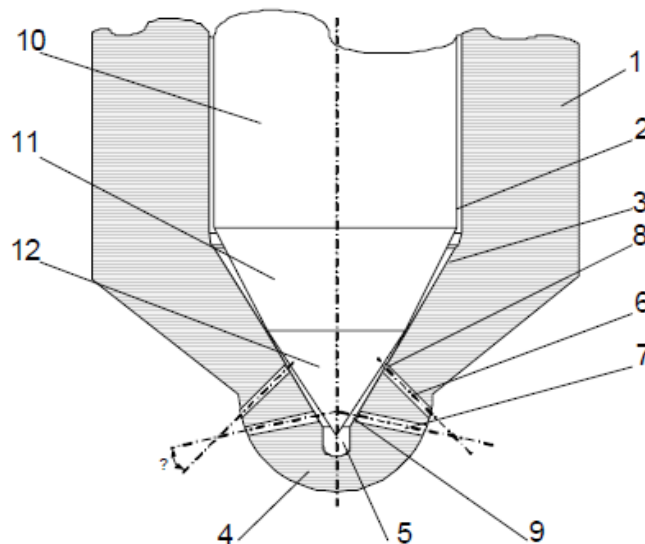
Схема розпилювача форсунки АЗП для роботи на рапсовому масло: 1 - корпус; 2 - циліндрична порожнина; 3 - конічна запірня поверхню корпусу; 4 - носок розпилювача; 5 – підголючна порожнина; 6 і 7 – розпилюють отвори; 8 і 9 - вхідні кромки отворів; 10 - голка; 11 – конічна поверхню голки; 12 - конічна запірня частина голки
